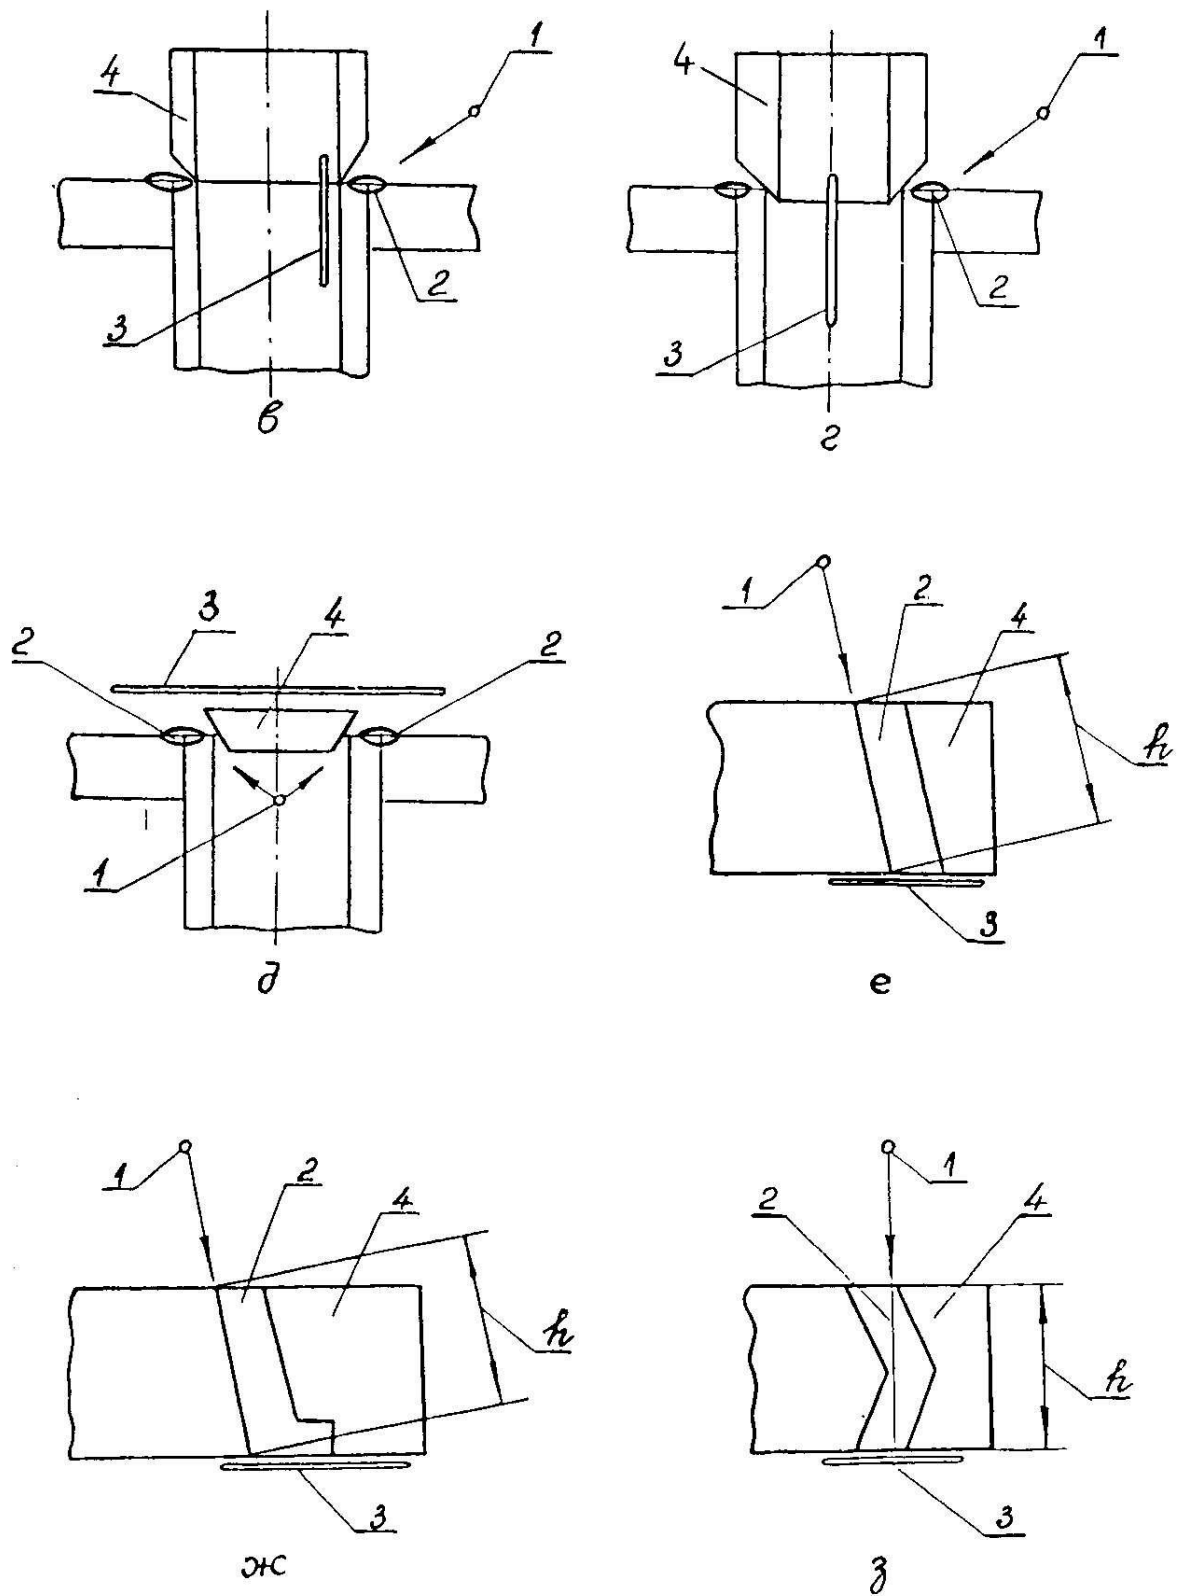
Схемы контроля сварных соединений вварки труб в трубные доски: 1- источник излучения; 2 - контролируемый участок; 3 - кассета; 4 - приставка-компенсатор; остальные обозначения см. рис. 2
